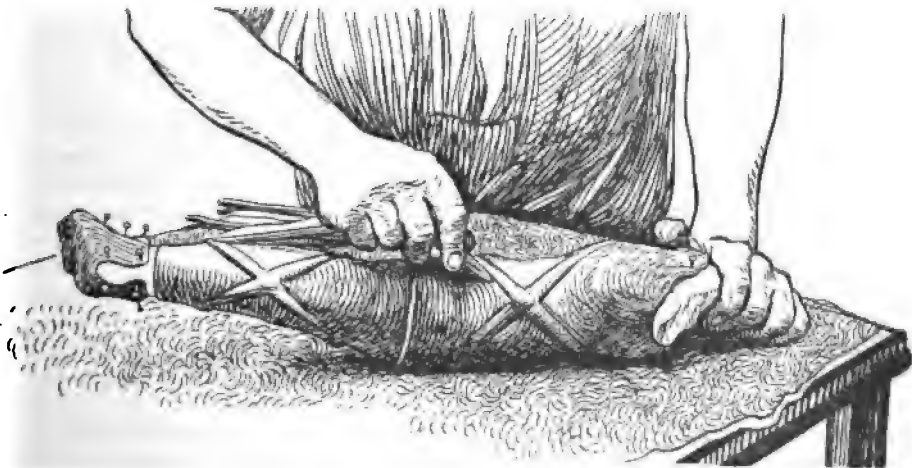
Bearbeitung des Leders mit dem Glättholz.
